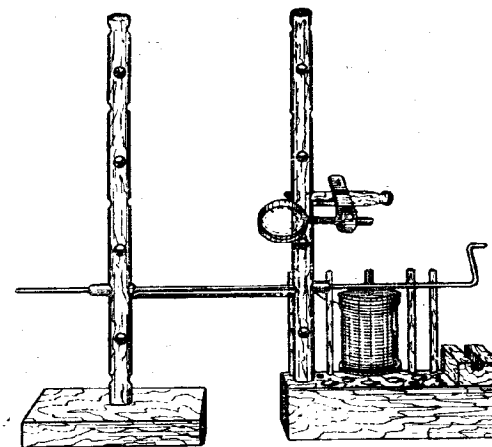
Приспособление для намотки спирали из нихромовой проволоки.
